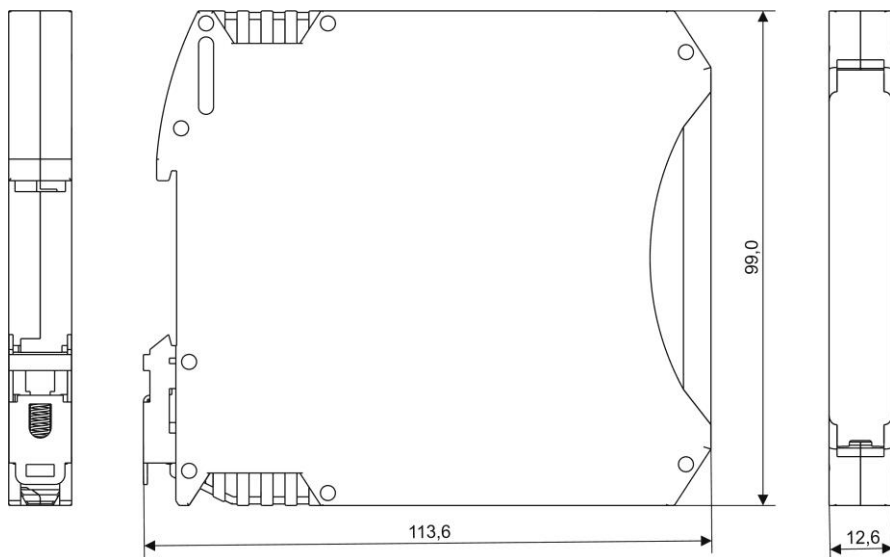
Габаритные размеры ИП 0304/M3-H-DIN
